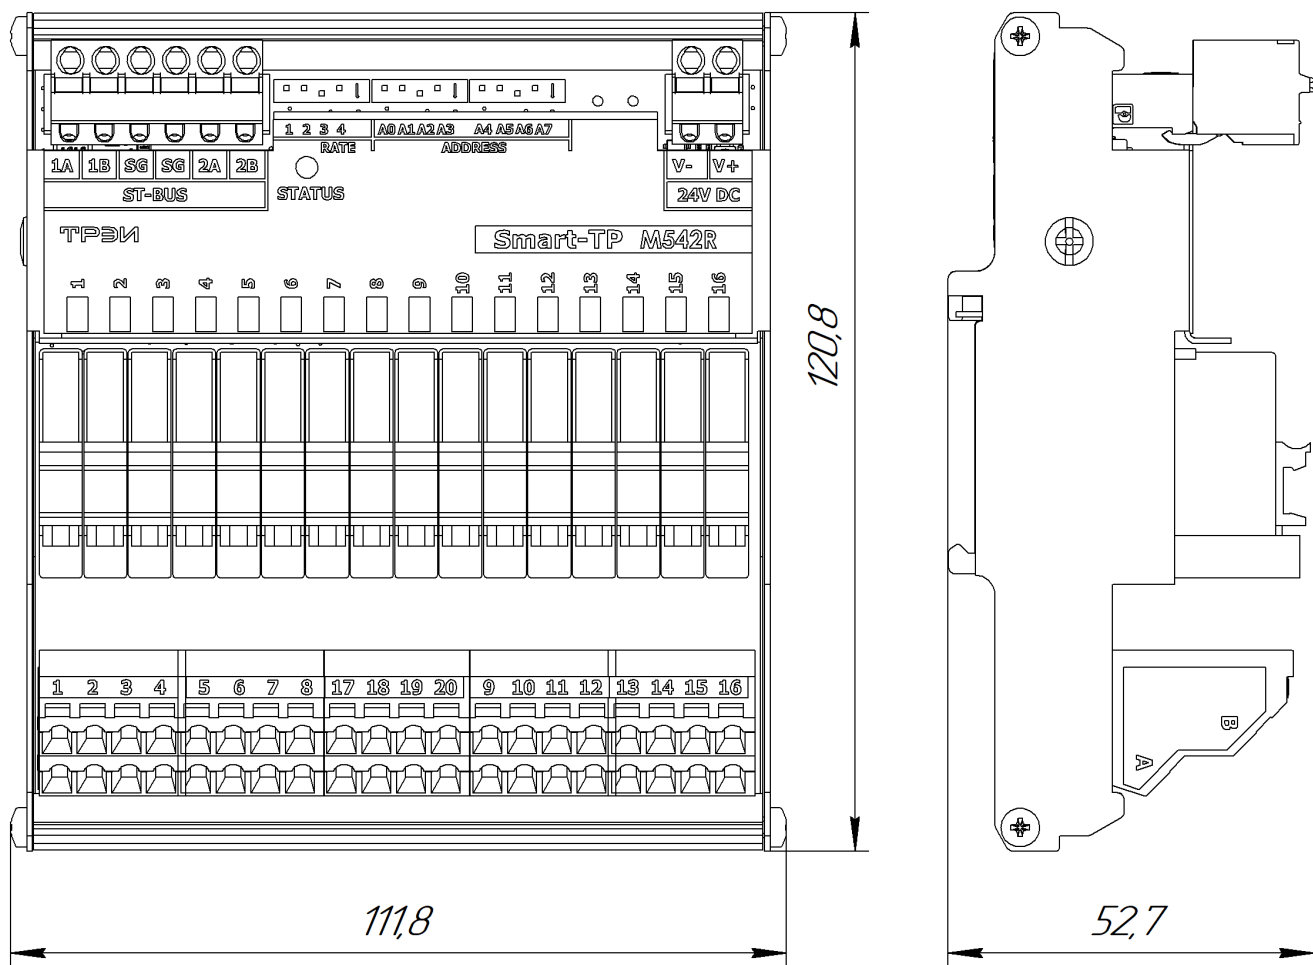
Чертеж общего вида M542R с указанием габаритных и присоединительных размеров
